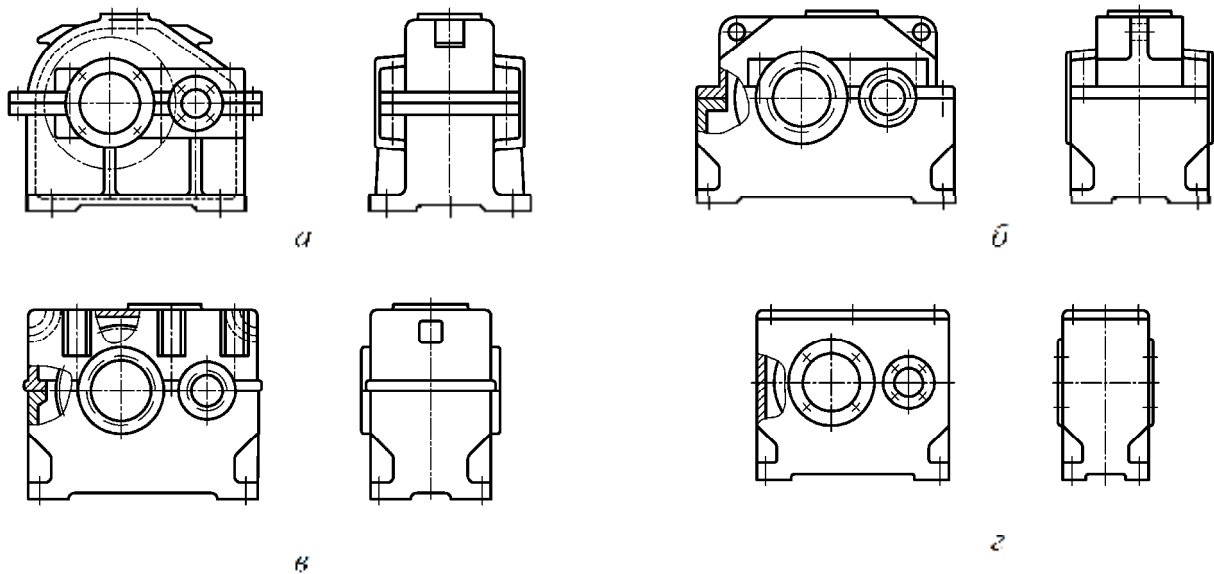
Конструктивное оформление корпуса редуктора
